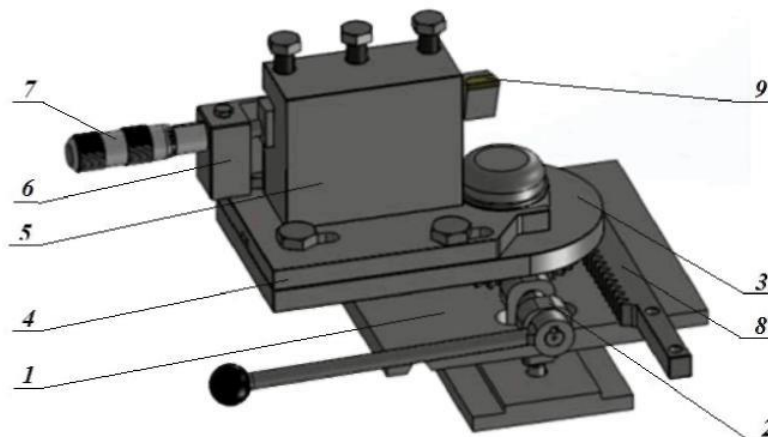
Загальний вигляд пристрою для токарної обробки неповних сферичних поверхонь: 1 – платформа; 2 – механізм фіксації; 3 – поворотний стіл; 4 – платформа поперечних переміщень різцетримача; 5 – різцетримач; 6 – кронштейн; 7 – мікрогеометричний гвинт; 8 – зубчаста рейка; 9 – різець.
